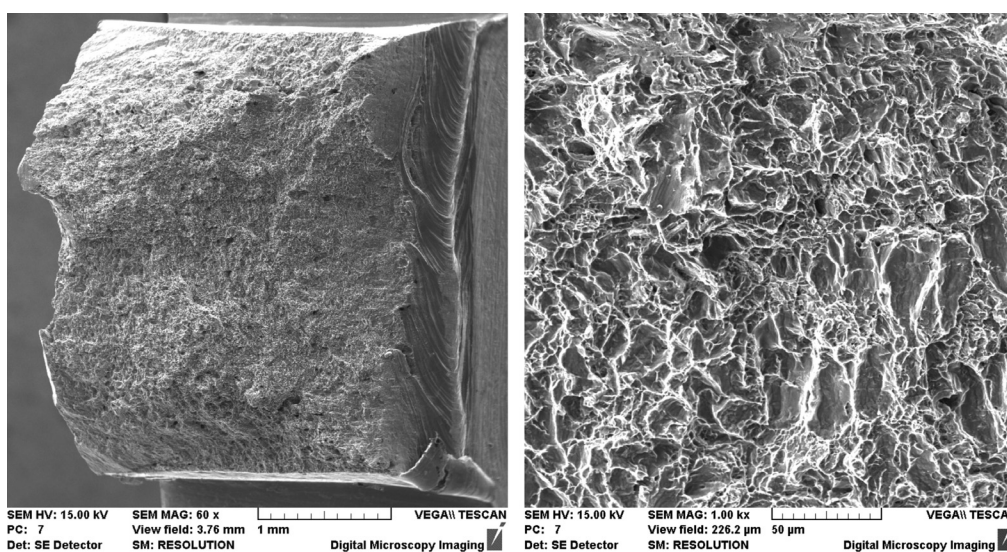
Рельеф поверхности разрушения образцов сплава ВТ1-0 со сварными швами после статического растяжения без добавления нанопорошков
